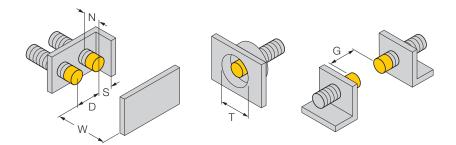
Minimale Montageabstände – Zylinderbauformen, nicht bündig einbaubar
